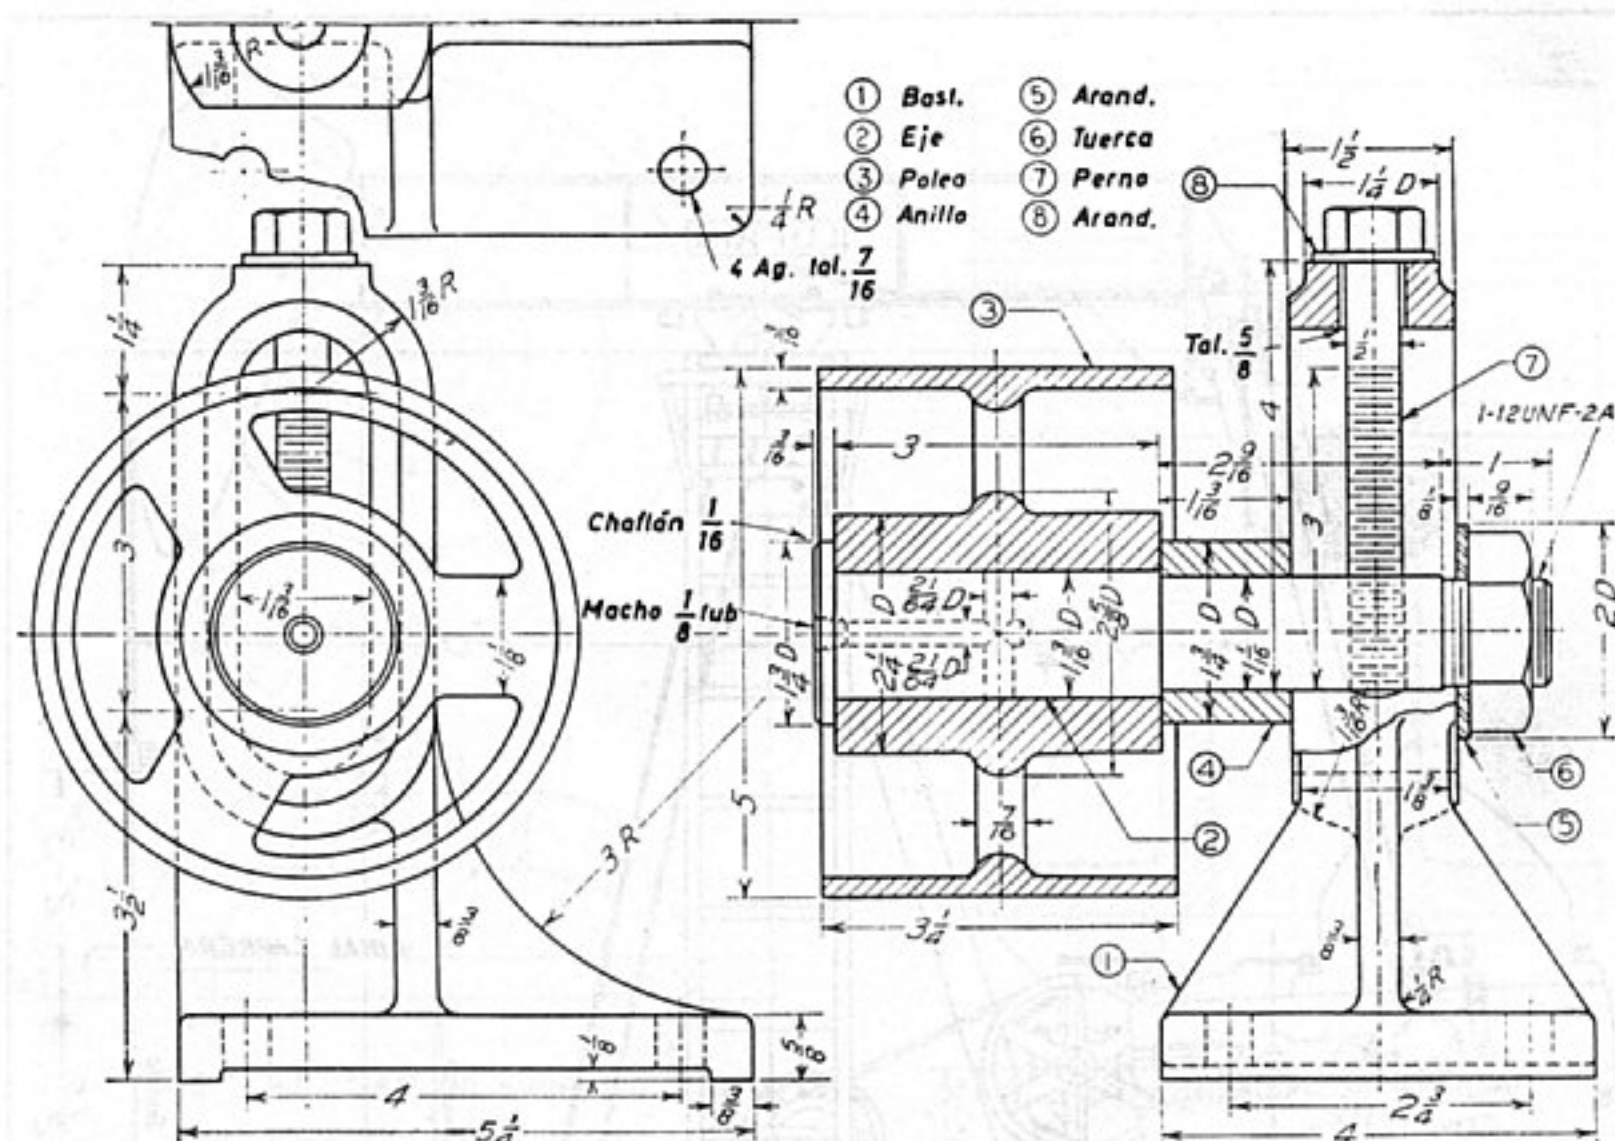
Ejemplo de un dibujo de conjunto.
